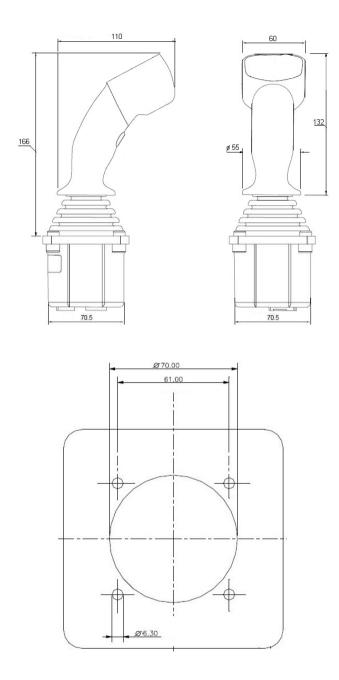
Габаритные размеры ДЖ и разметка места для его установки
